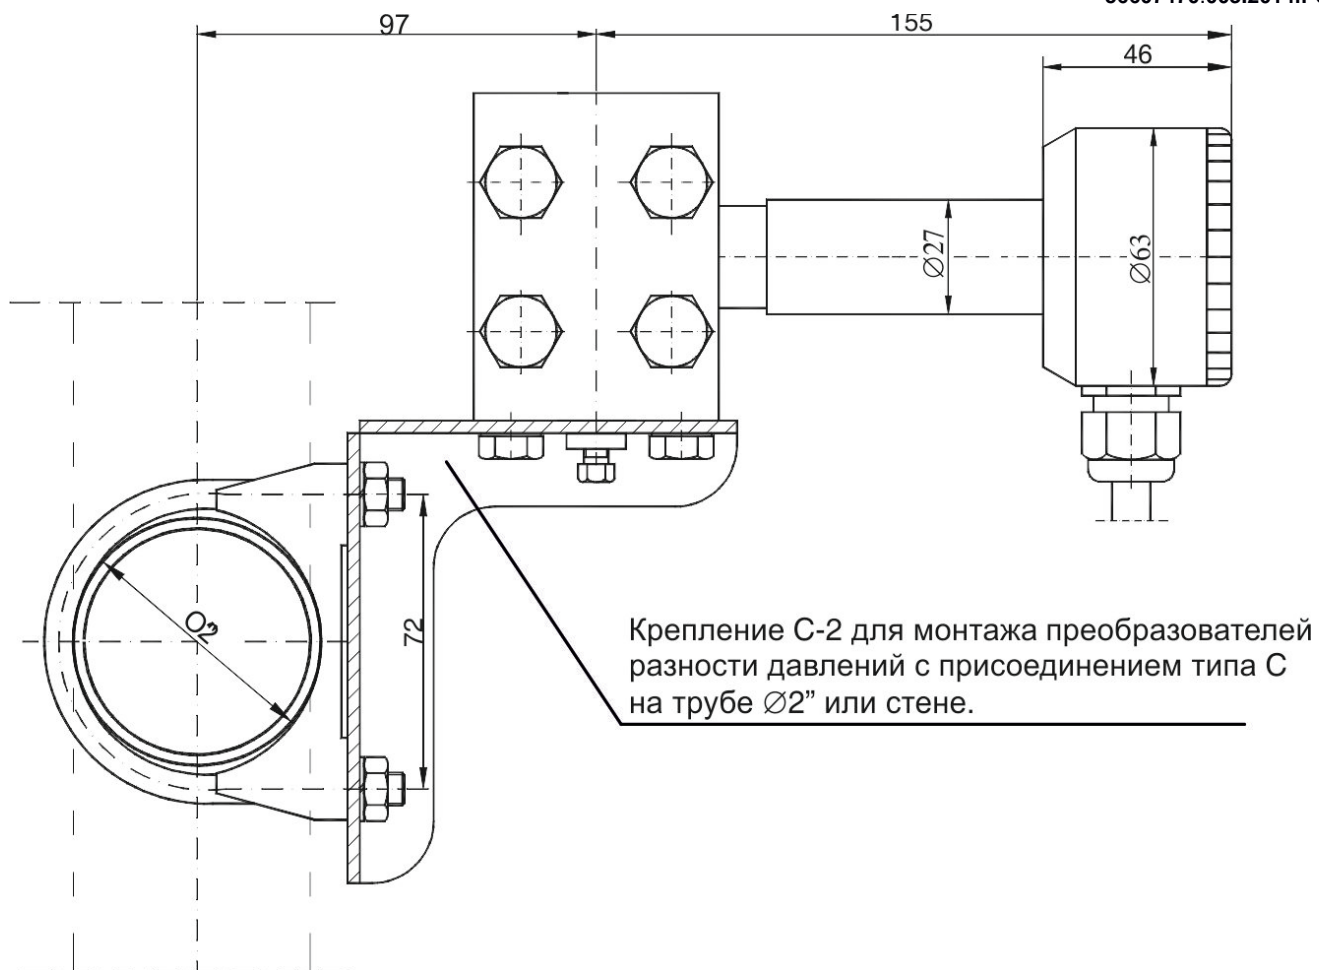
Способ крепления преобразователя PR-28 с присоединением типа С.
